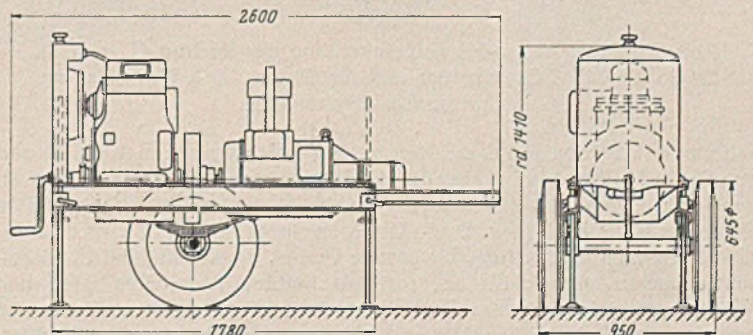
Dieselschweißumformer der Siemens-Schuckertwerke AG. für Schweißströme von 40 bis 250 A bei 20 bis 25 V.
